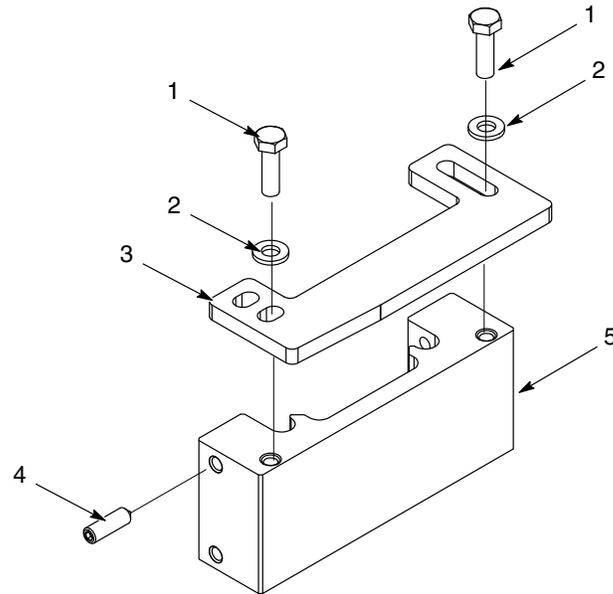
Installieren und Ausrichten der Behälter-Niederhalter
